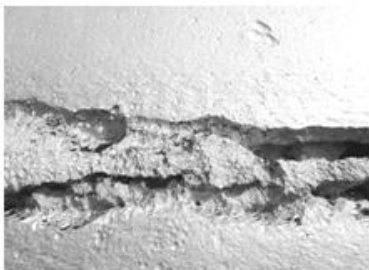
Сквозная ножевая коррозия в сварных швах хранилища  $\text{HNO}_3$ .
